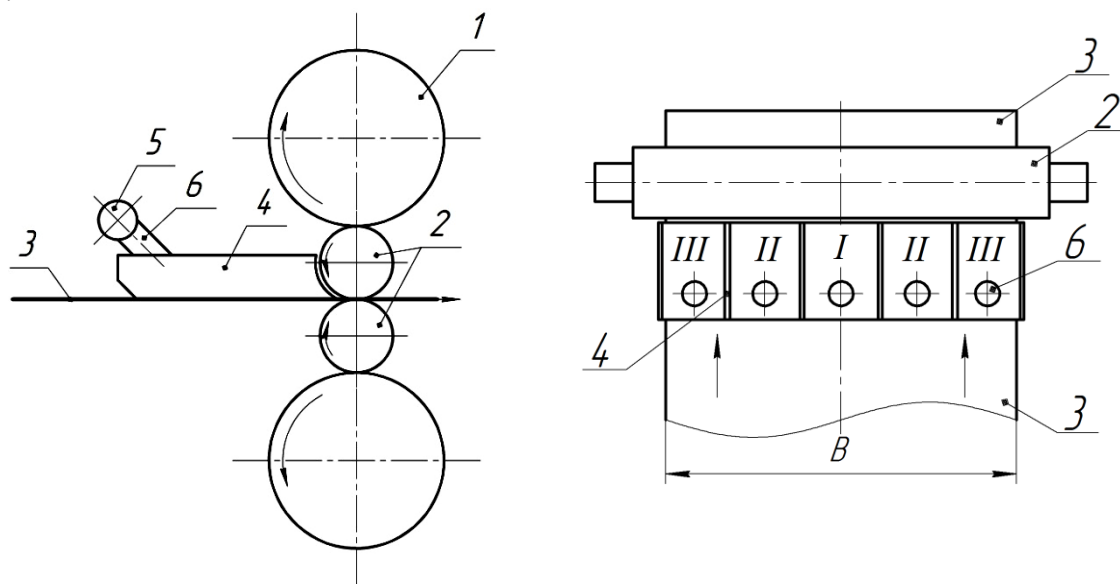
Схема пристрою для диференційованого подання охолоджувача на штабу: 1 - опорний валок; 2 - робочі валки; 3 - штаба; 4 –перегородки ; 5 - колектор; 6 – трубка для подачі охолоджувача
